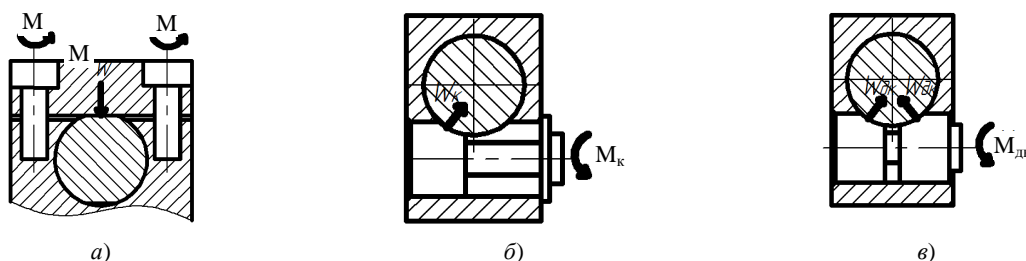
Механизмы закрепления резцового блока в корпусе:
